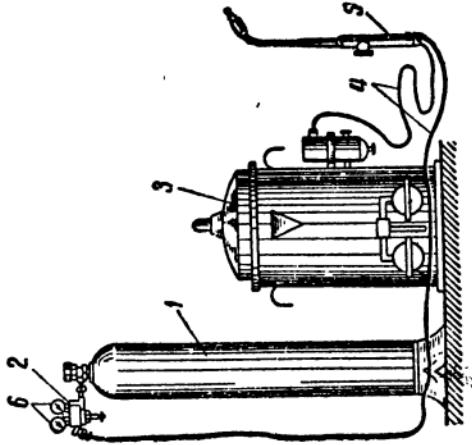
Газосварочная установка с ацетиленовым переносным газогенератором:
